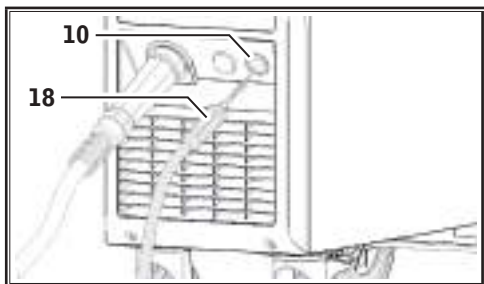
Подключение кабеля для заземления обрабатываемой детали
